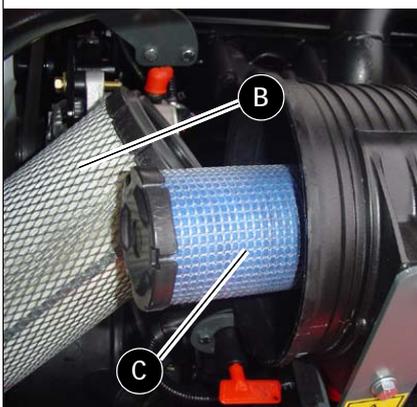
Desmontaje/montaje del elemento de filtro interior
